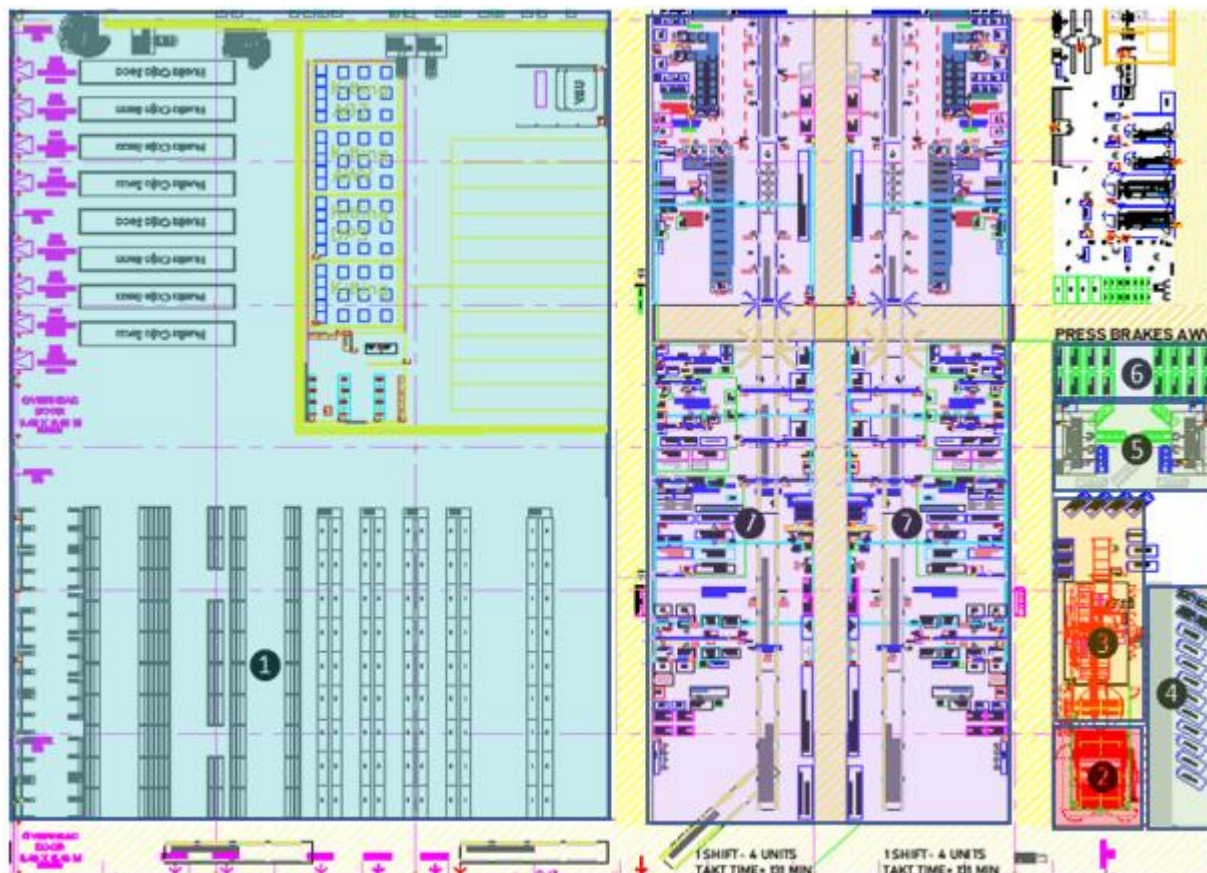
LayOut General de Procesos de fabricación previos a ensamble
